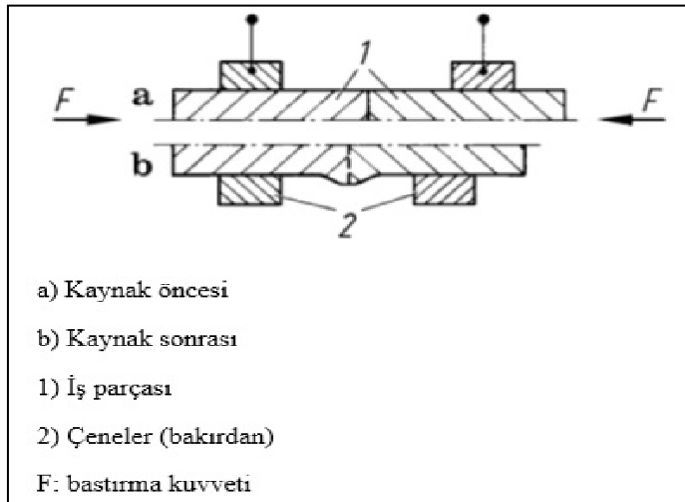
Testere lamasının alın kaynağı ile kaynaklanması [33]
